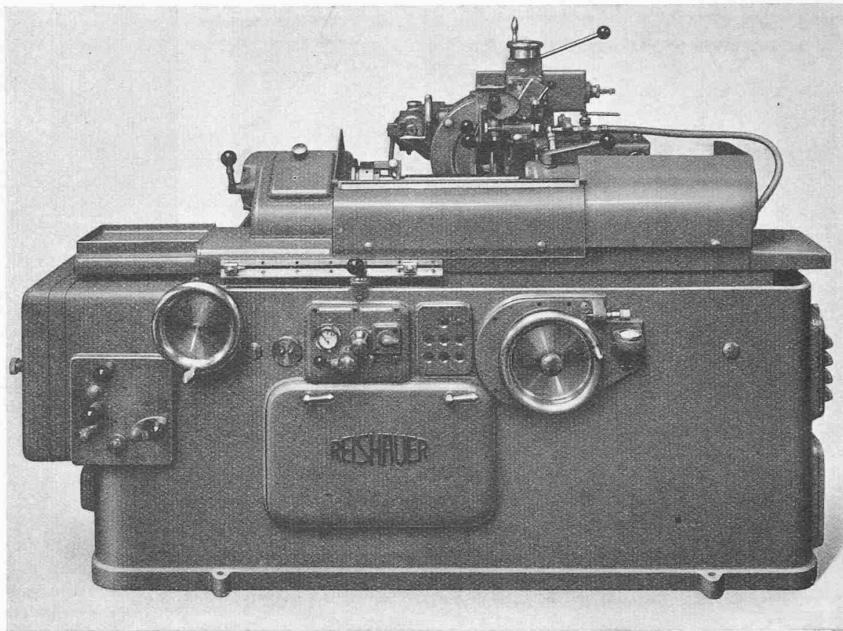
Universal-Gewinde- und Schneckenschleifmaschine Reishauer Typ NRK
